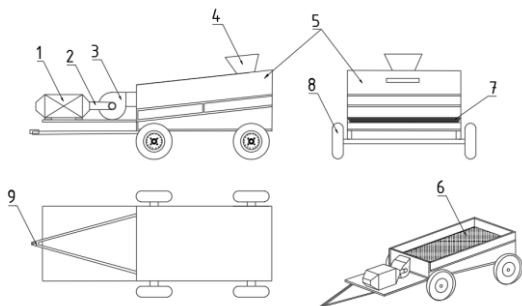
Конструкция передвижной конвективной сушильной установки. 1 – калорифер; 2 – газоход; 3 – центробежный вентилятор; 4 – загрузочный бункер; 5 – металлическая крышка; 6 – сито; 7 – поддон для семян; 8 – опорные колеса; 9 – тягово-сцепное устройство.
